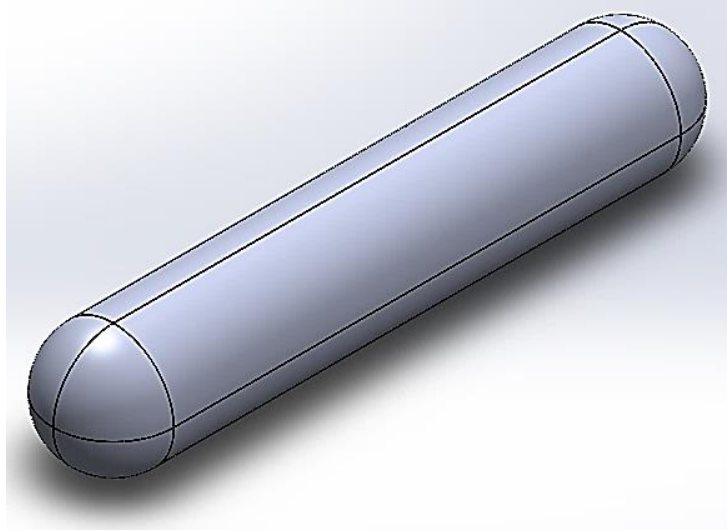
Vista isométrica del tanque a presión ensamblado
